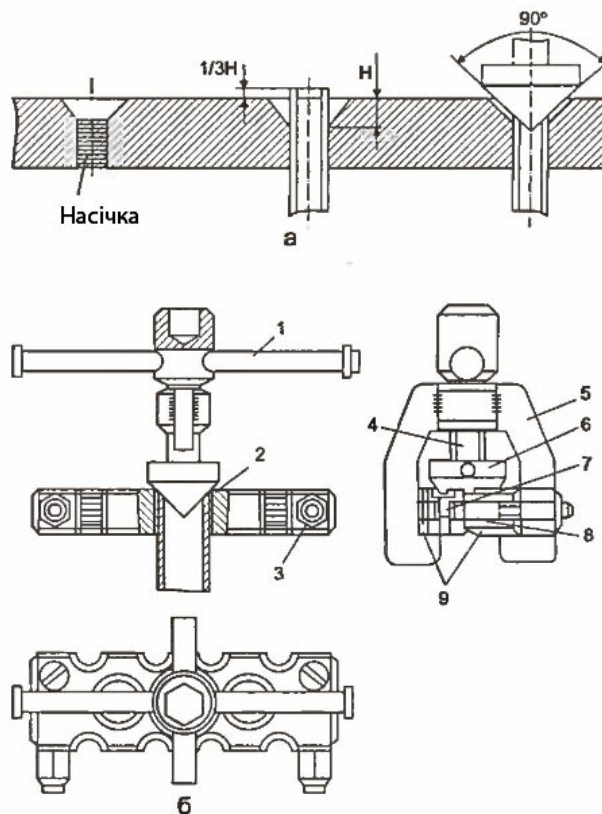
Бортувальна колодка для мідних трубок: а-схема бортування, б-пристрій для бортування. 1-головка силового гвинта, 2-оброблювана трубка, 3-зажим, 4-силовий гвинт, 5-захват, 6-конус-пуасон, 7-вісь болта, 8-спеціальний болт, 9-губки
